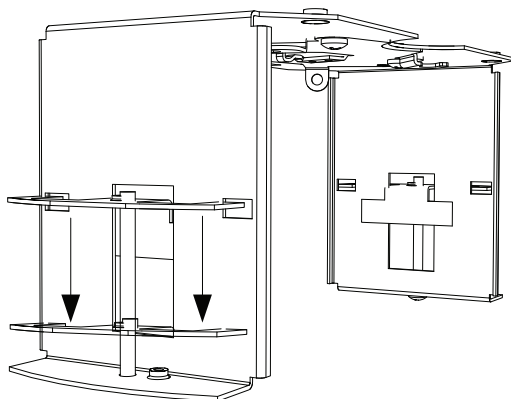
Befestigen der Montageplatte an der Befestigungshalterung
